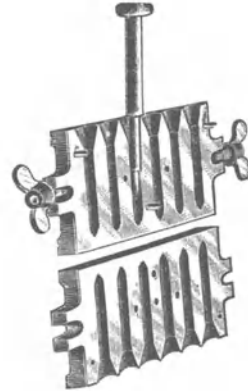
Maschine für Voll- und Hohl-Suppositorien.
